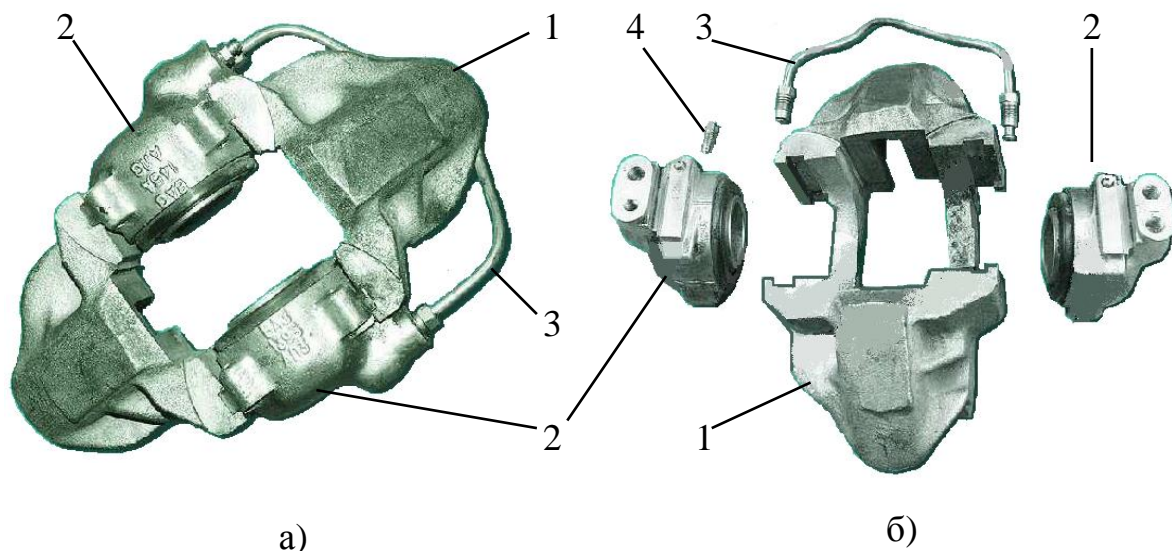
Суппорт в сборе (а) и детали суппорта (б): 1 – корпус суппорта; 2 – рабочие тормозные цилиндры; 3 – соединительный трубопровод; 4 – фиксатор
